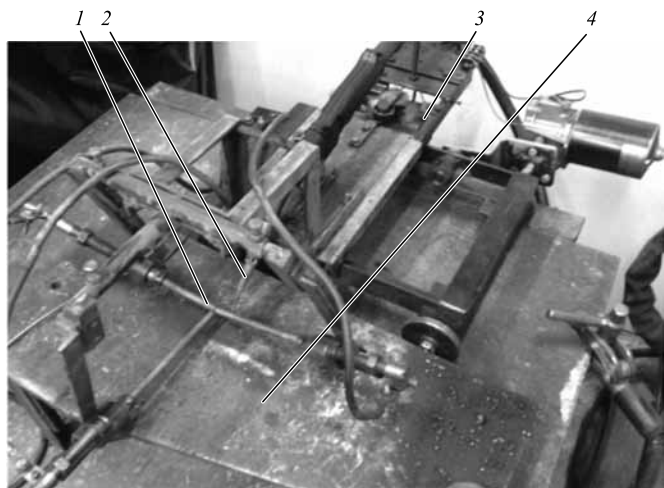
Установка автоматической наплавки порошковой проволокой с опережающей трехфазной дугой:
